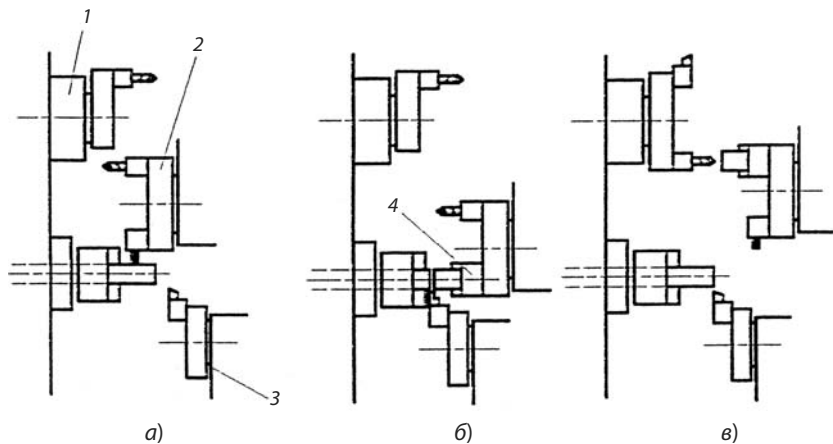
Последовательность обработки заготовки на станке с тремя револьверными головками:
